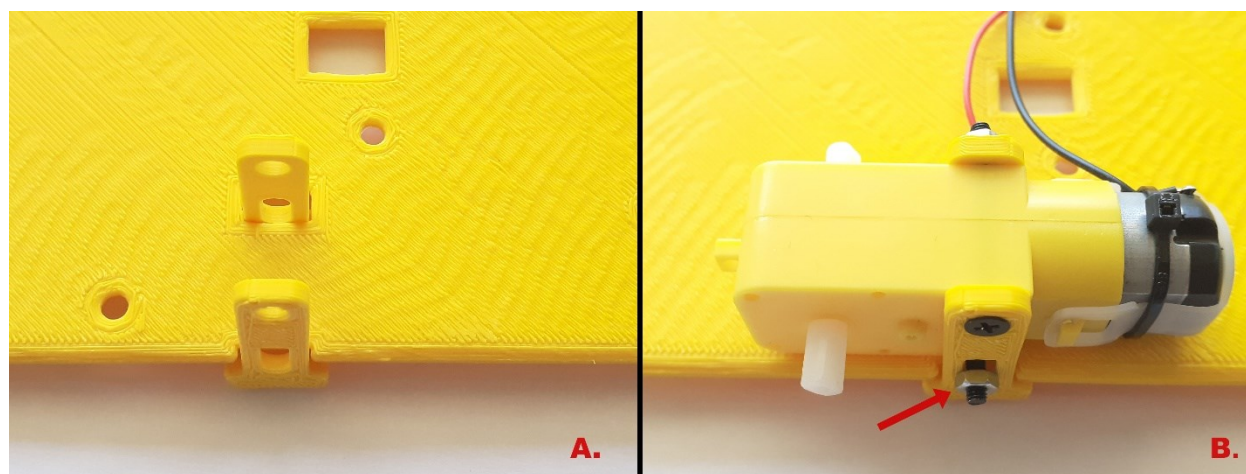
A. Placement des deux supports/attaches sur le châssis ; B. Fixation du moteur à engrenages DC en utilisant les supports, les deux vis de 30 mm et les deux écrous
